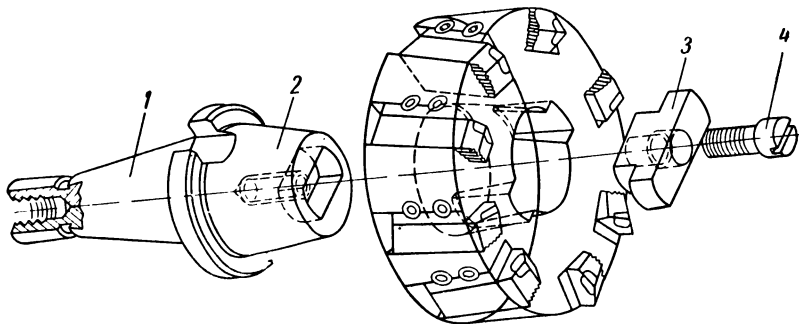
Концевая оправка для фрез с конусным посадочным отверстием
